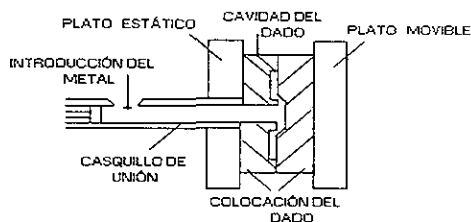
Representación esquemática de cámara fría en un proceso de fundición a presión.
